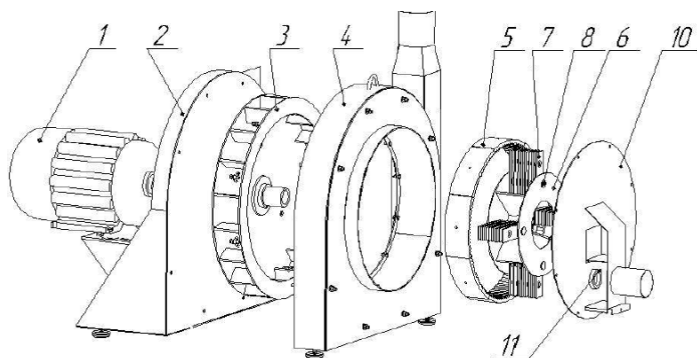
Детализация дробилки (модель ДКР): 1 – электродвигатель; 2 – крышка со станиной эл.двигателя; 3 – диск вентилятора (выбрасывающая дорожка не показана); 4 – корпус дробилки; 5 – деки; 6 – ротор; 7 – молотки; 8 – ось молотков; 10 – крышка передняя с сепаратором; 11 – магнит.
